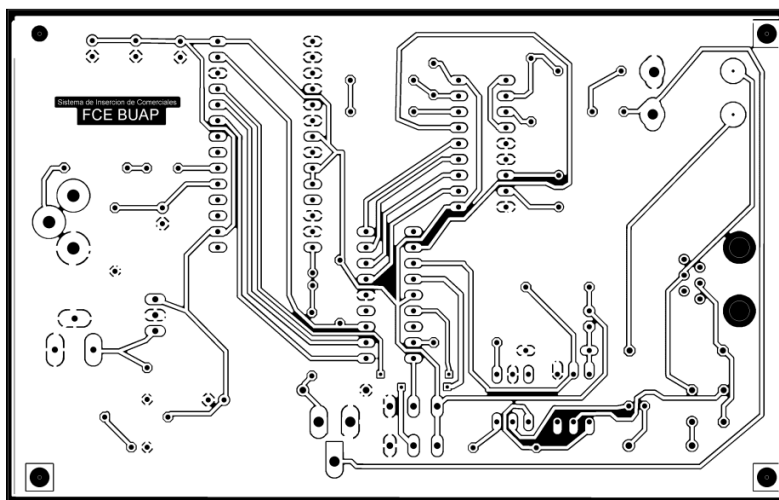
Placa de circuito impreso corregida, lado soldaduras, en negativo. (No está a tamaño real)
